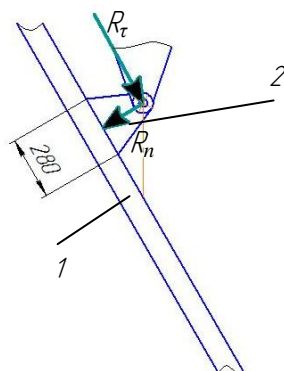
Схема для розрахунку зварного шва: 1 – вухо осі; 2 – рама
